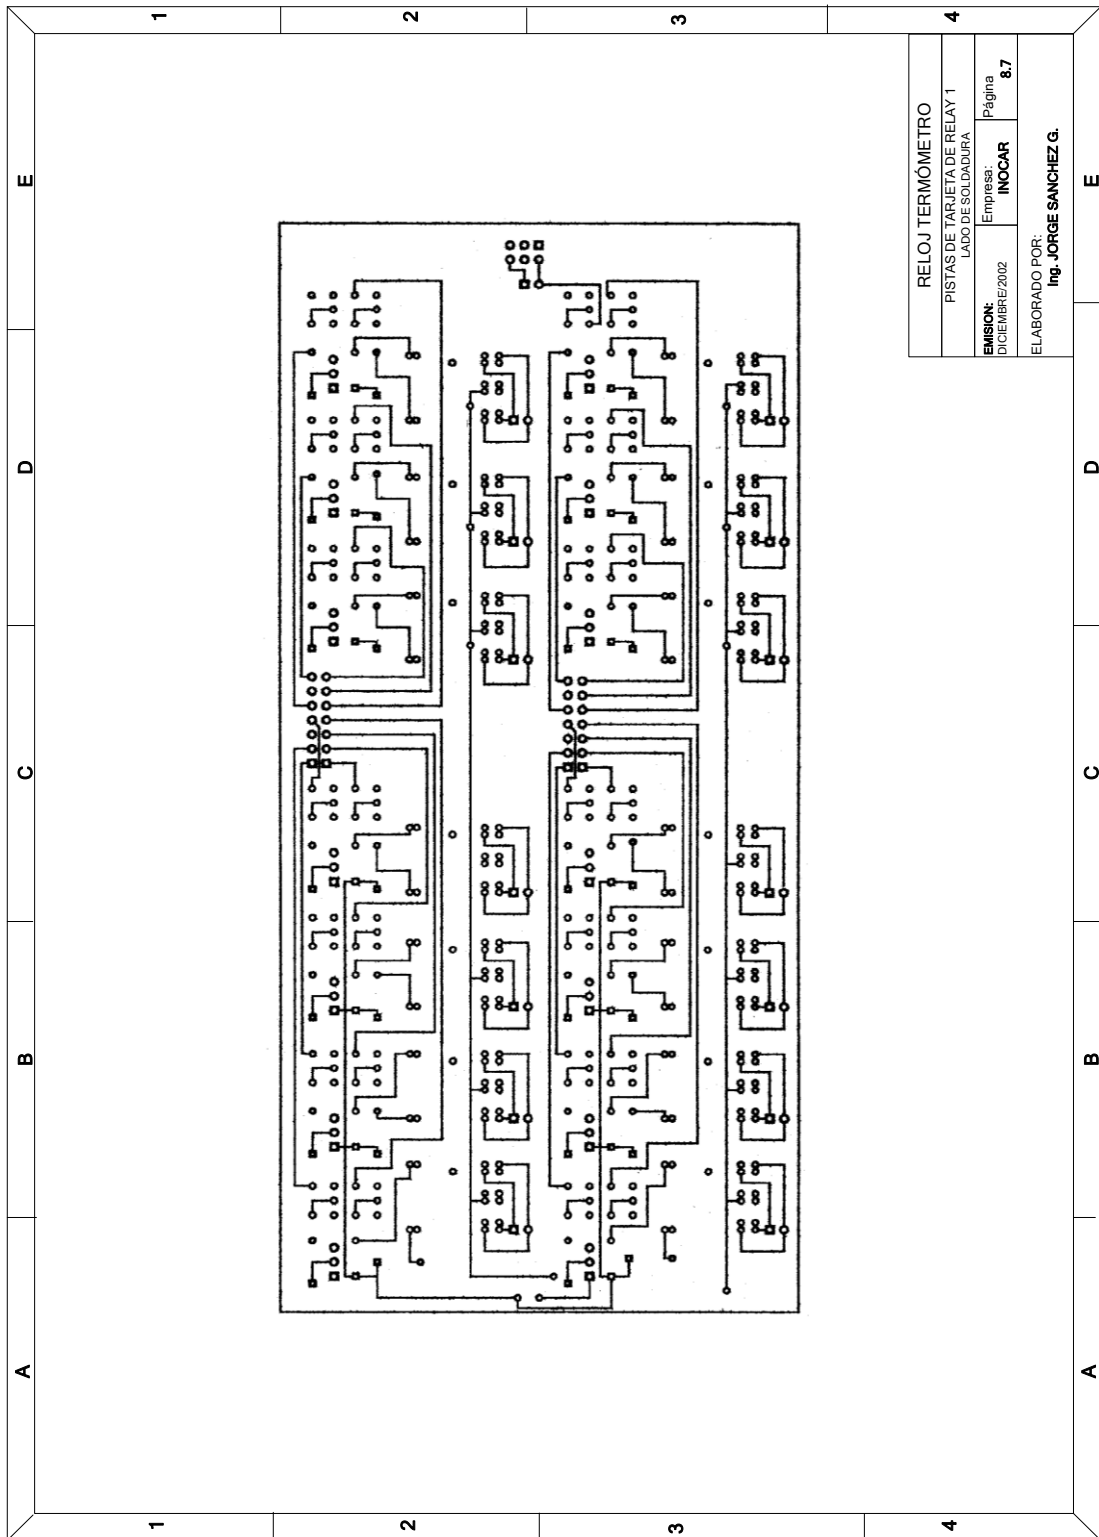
Tarjeta de relay 1 (Pistas lado de soldadura)
